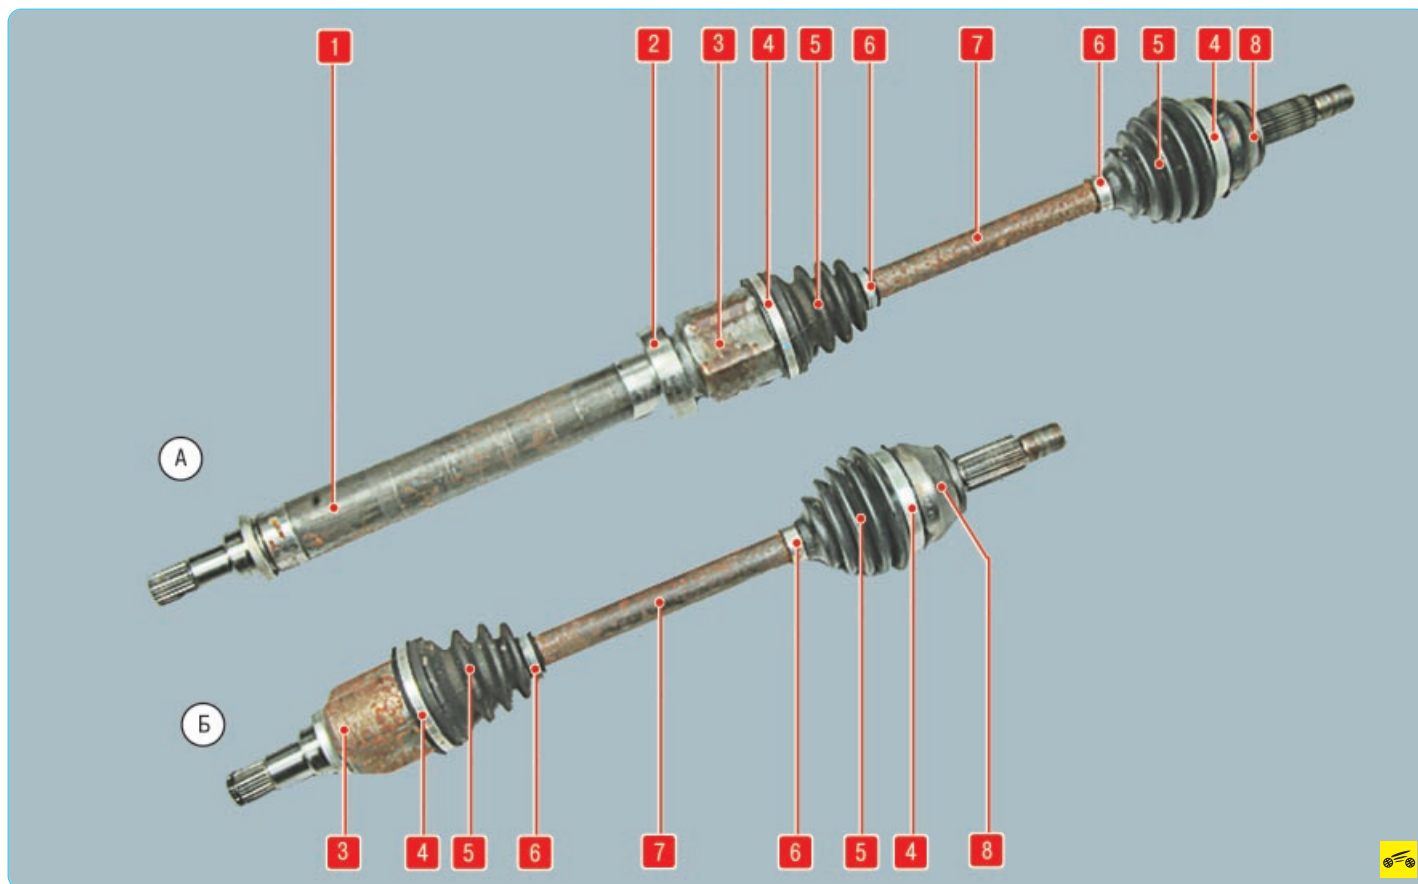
Приводы передних колес: А – привод правого переднего колеса; Б – привод левого переднего колеса; 1 – промежуточный вал; 2 – подшипник промежуточной опоры; 3 – внутренние шарниры равных угловых скоростей; 4 – большие хомуты крепления чехлов шарниров; 5 – чехлы шарниров; 6 – малые хомуты крепления чехлов шарниров; 7 – вала приводов; 8 – наружные шарниры равных угловых скоростей
